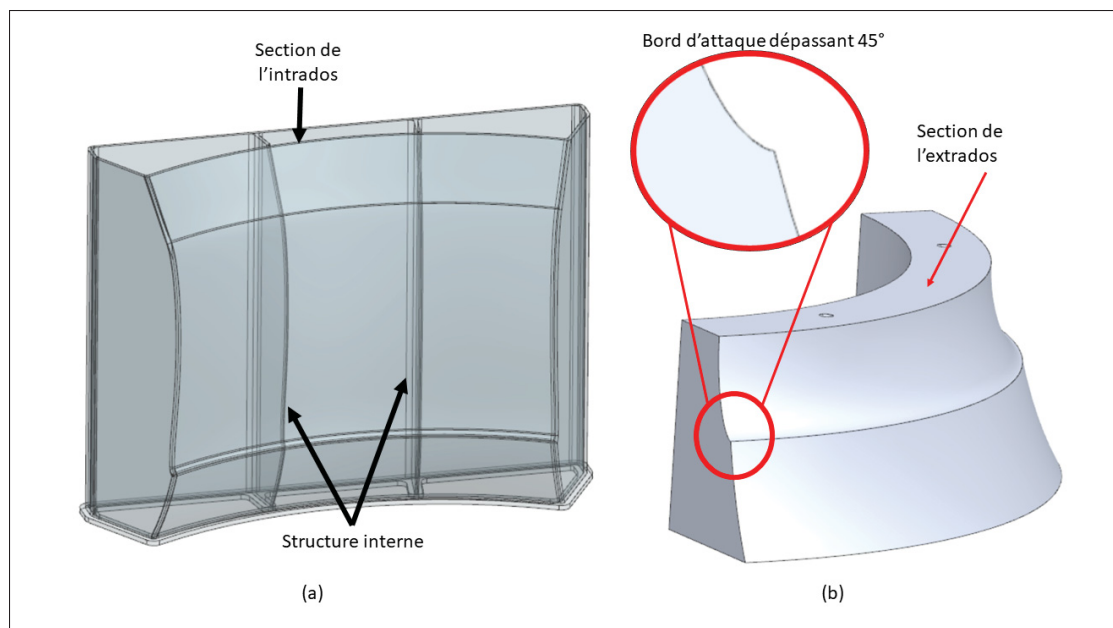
Dessins des sections du moule identifiant : (a) les structures internes, (b) le bord d'attaque
